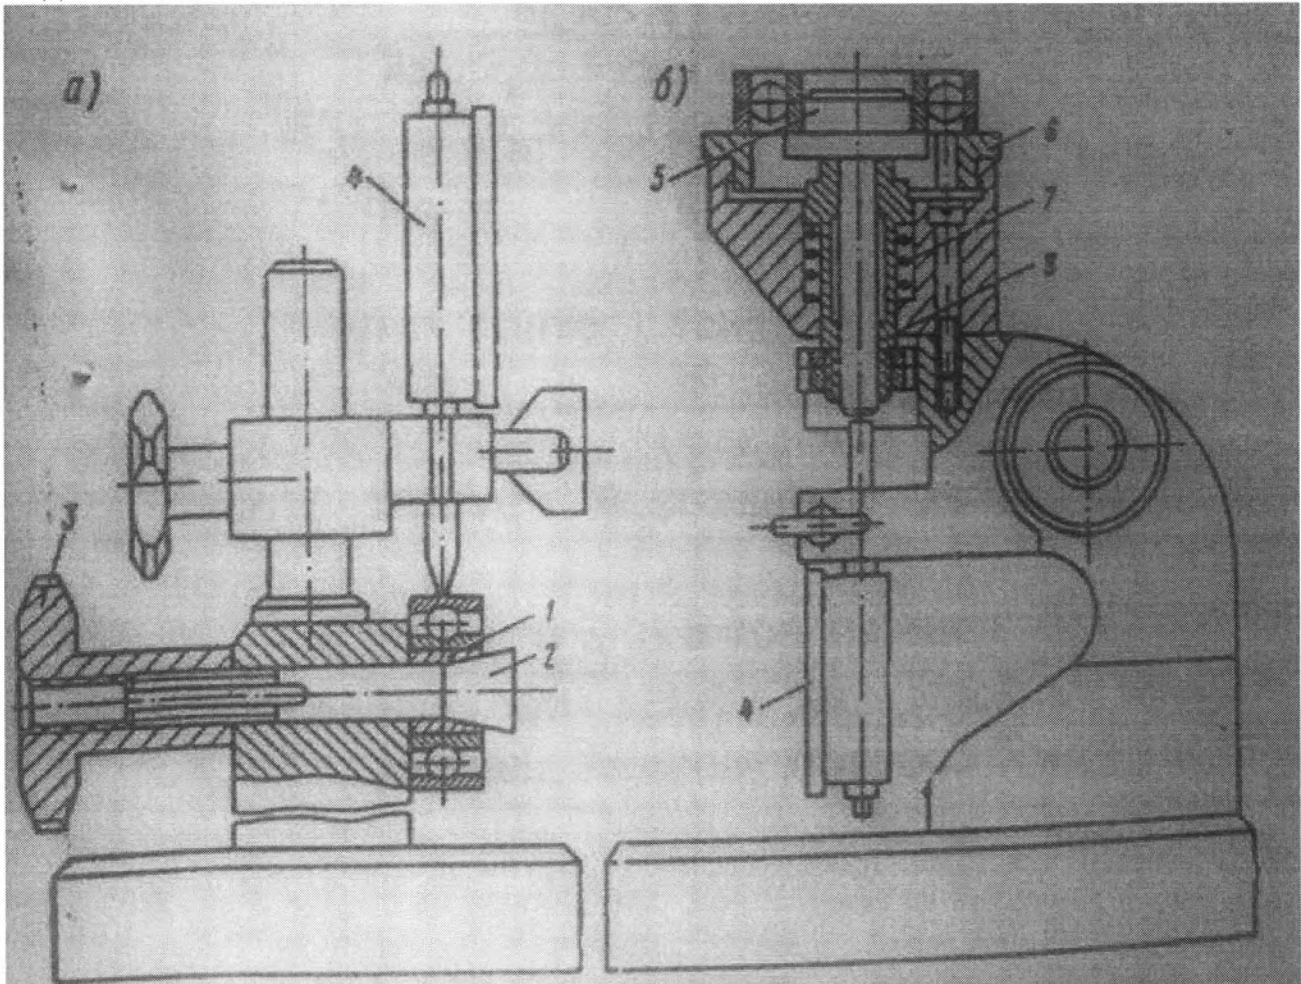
Приспособление для контроля зазоров в шариковых подшипниках:
